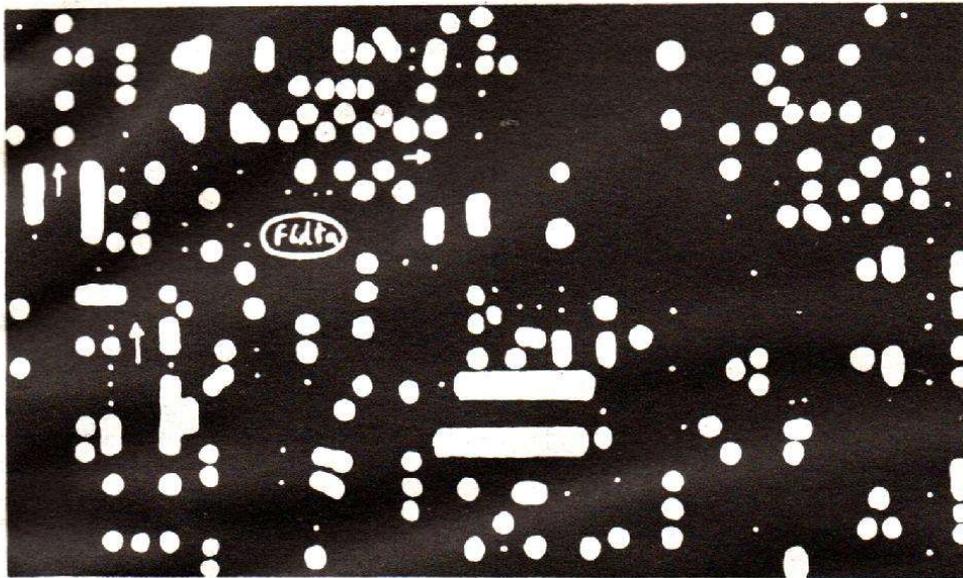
Circuit imprimé du récepteur (vue de dessus).
